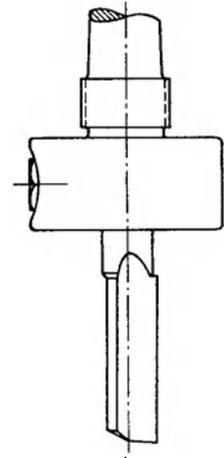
Zentrisches Spannfutter mit hinterdrehtem Fräser.
